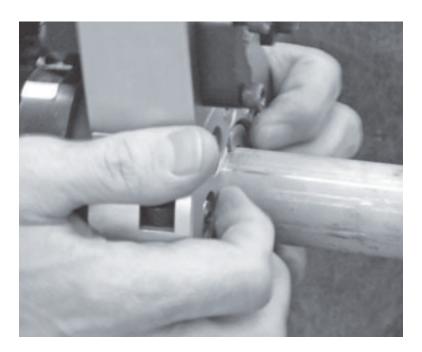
Glissez la bague de serrage dans la machine SDSF à proximité de la ligne de coupe.
